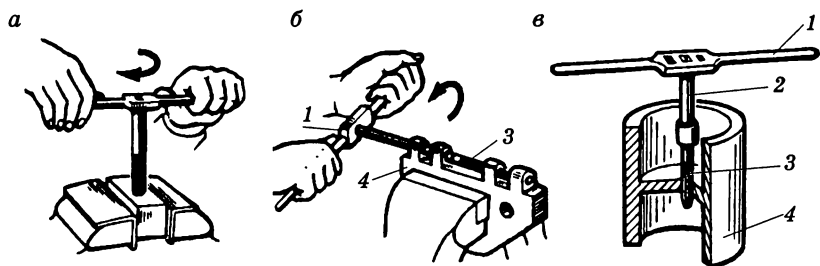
Приемы развертывания отверстий ручными развертками:
